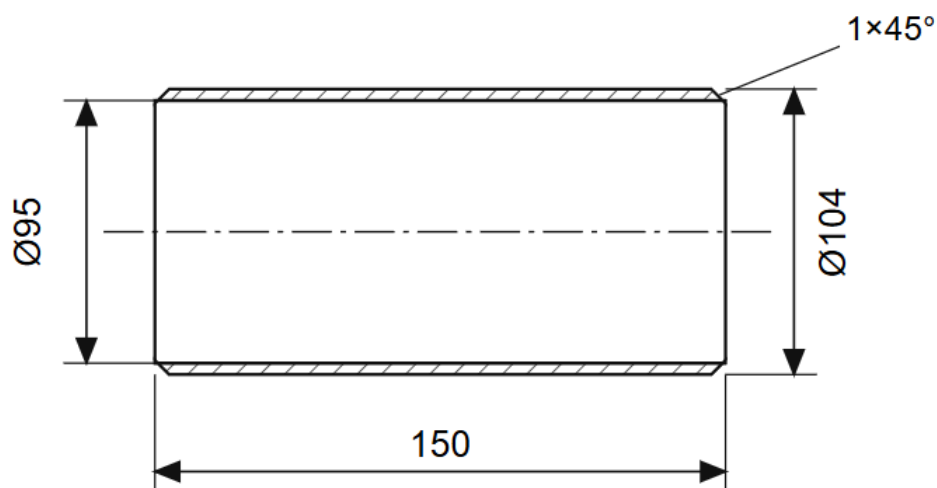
Ескіз корпусу ролика (обичайки)
